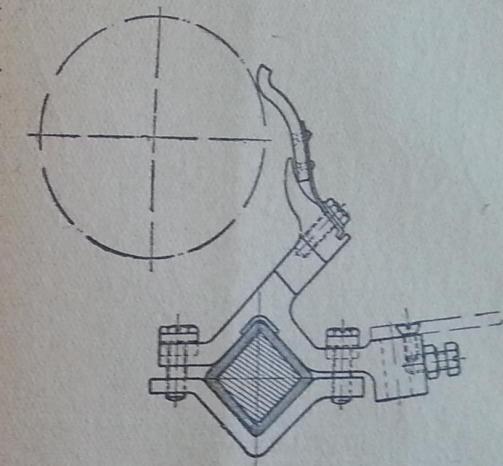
Контакт реверсивно-тормозного барабана контроллера ДТ-41.
